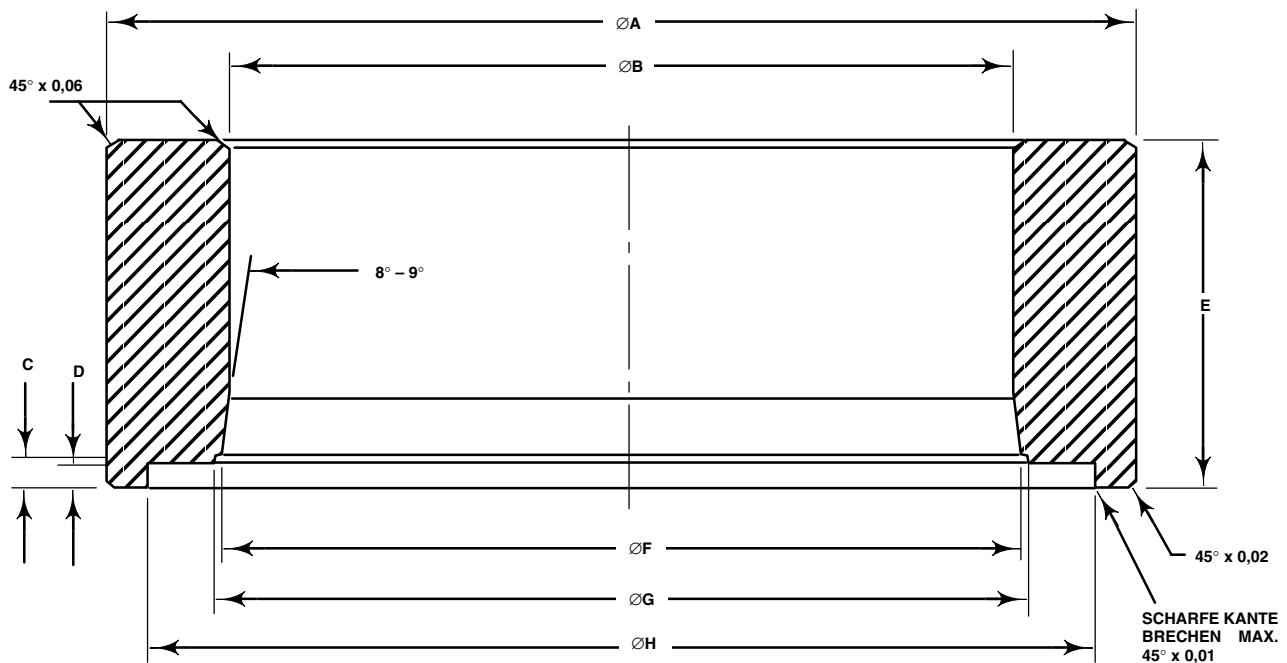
Einbauwerkzeug für die C-seal™ Kegeldichtung
